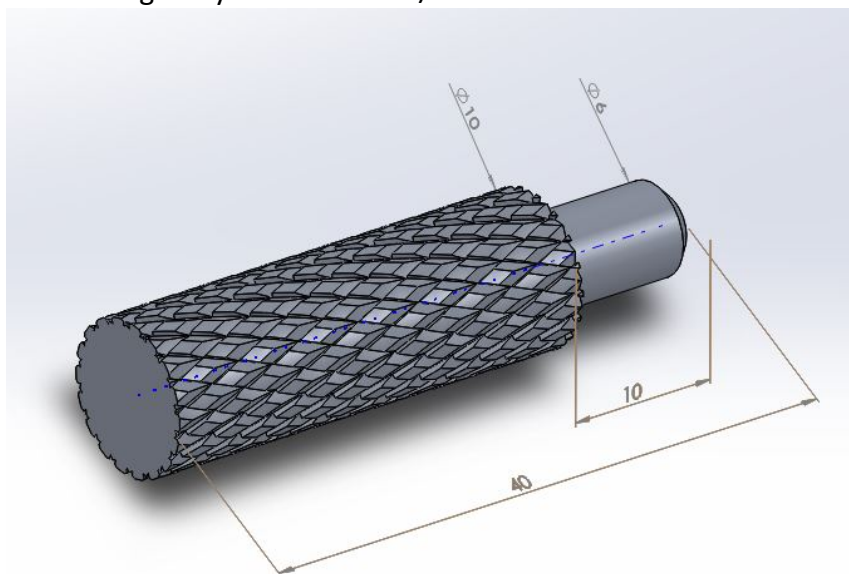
Redondo y moleteado. Estribo punta estribera.
